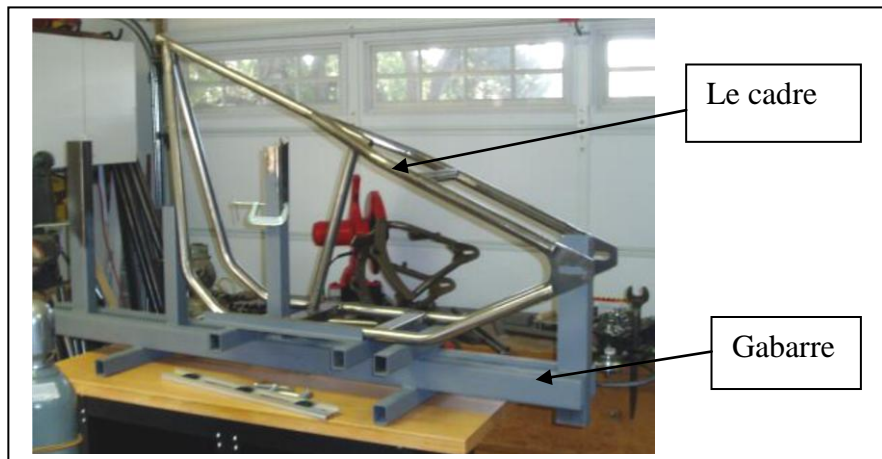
Gabarret d'assemblage des cadres motos [2]
